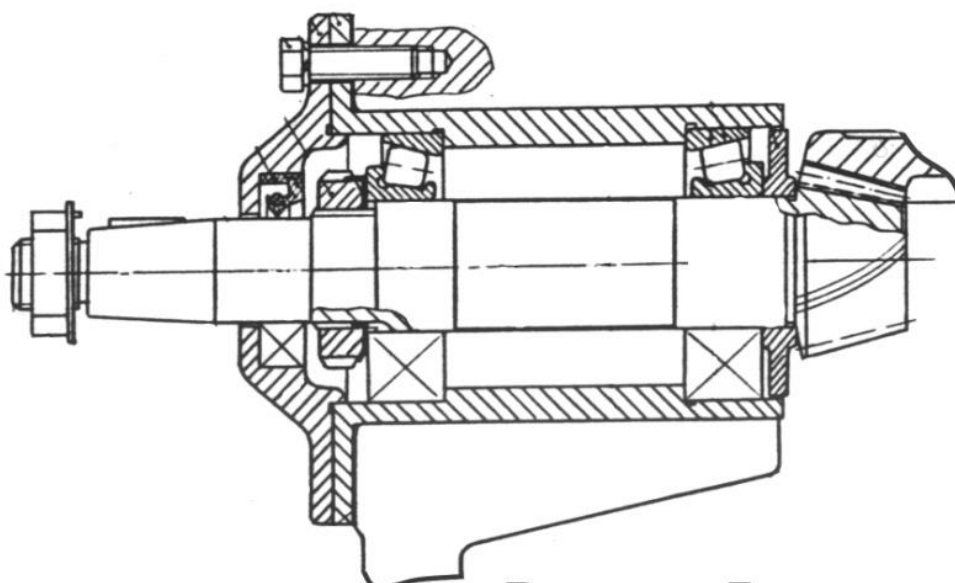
Узел вала-шестерни конической в стакане (вариант-б)
